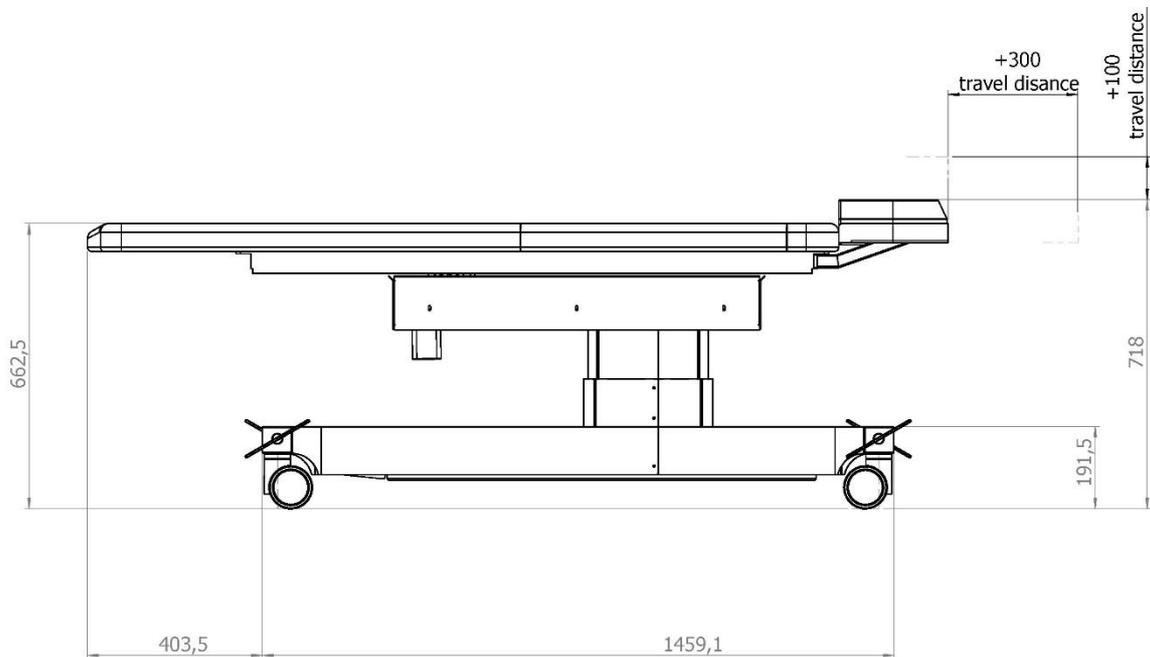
Dimensions Patient Bed – vue latérale
